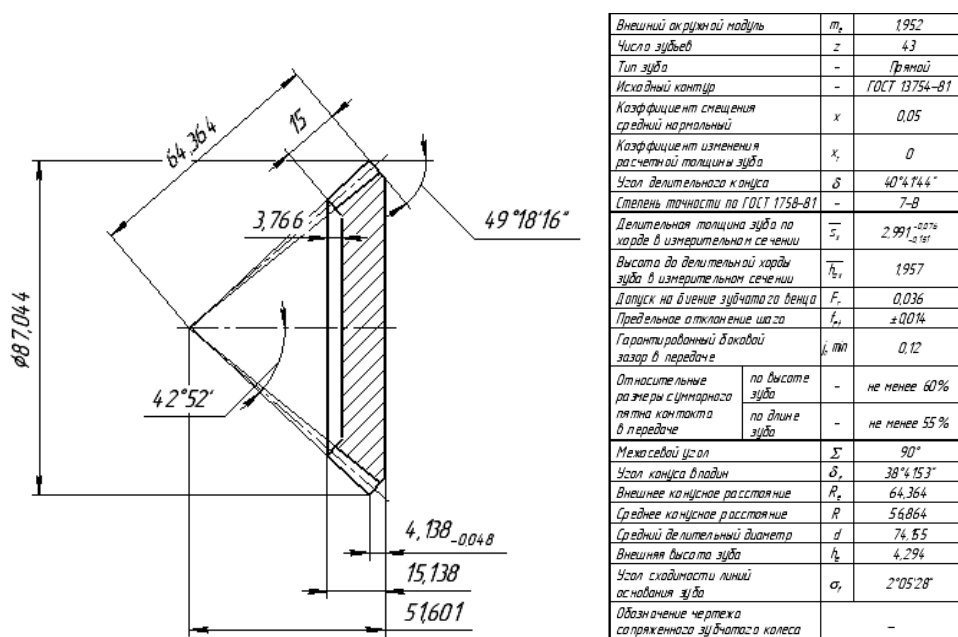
Чертеж конической шестерни с прямыми зубьями
